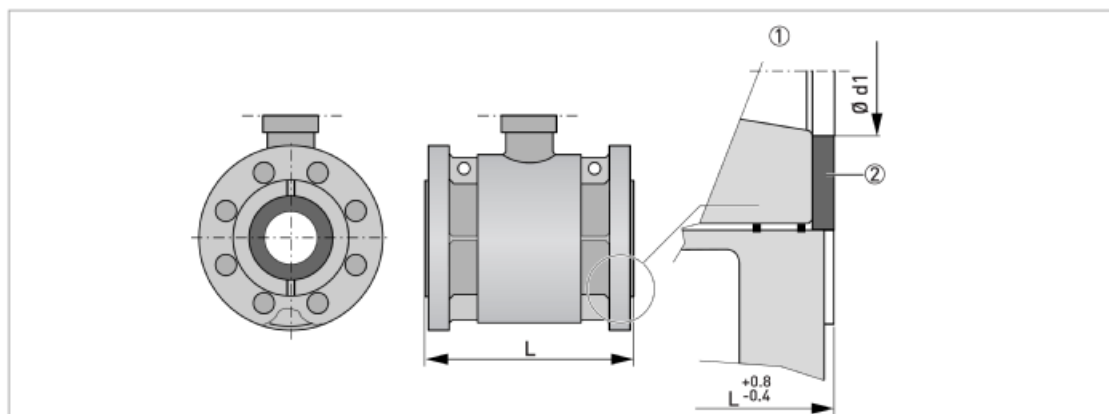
Элементы конструкции фланцевой версии DN 25 ... 100
